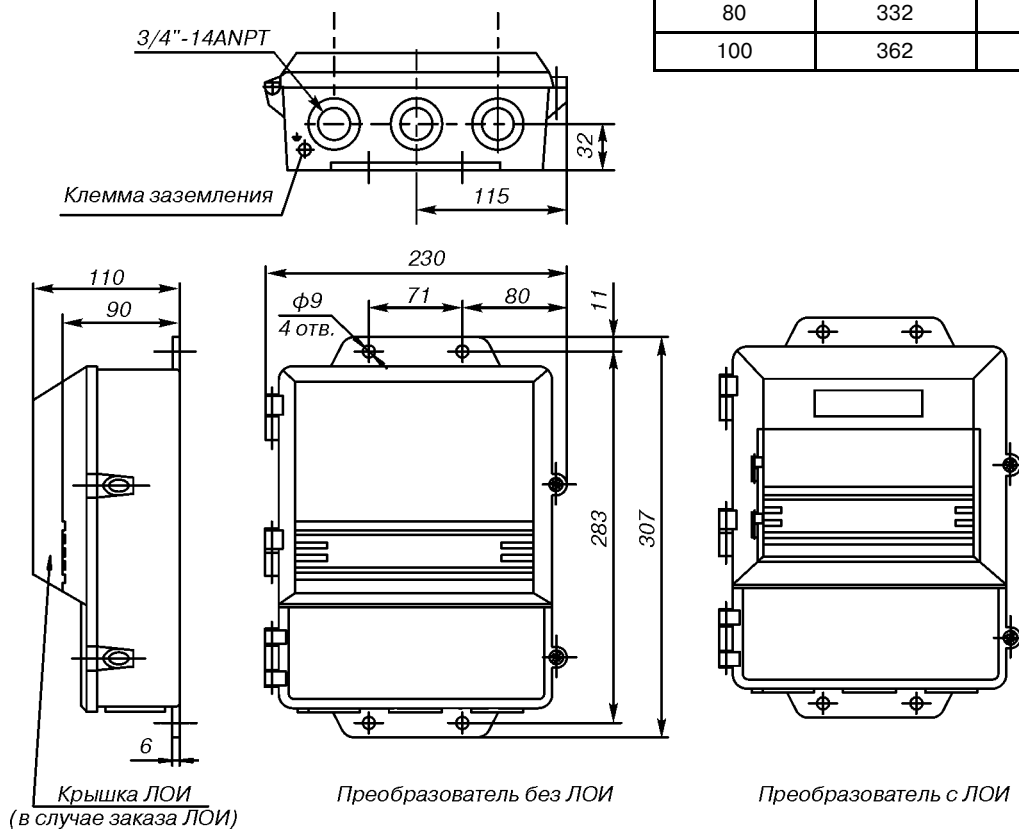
Габаритные и присоединительные размеры преобразователя 8712D.
